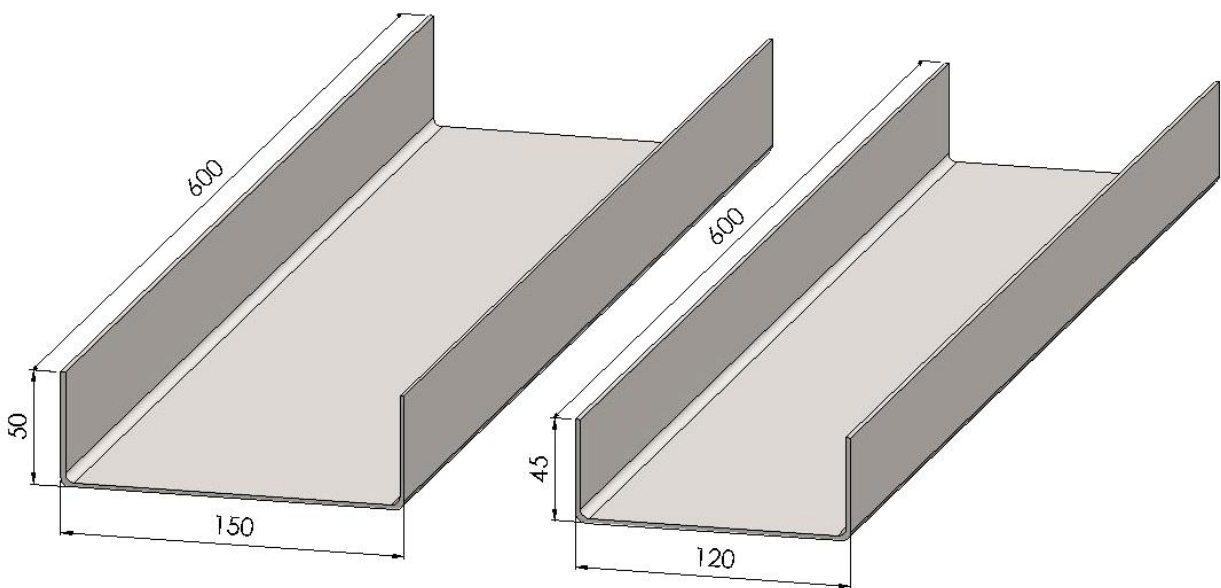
Dimensões em (mm) das seções transversais dos perfis U
